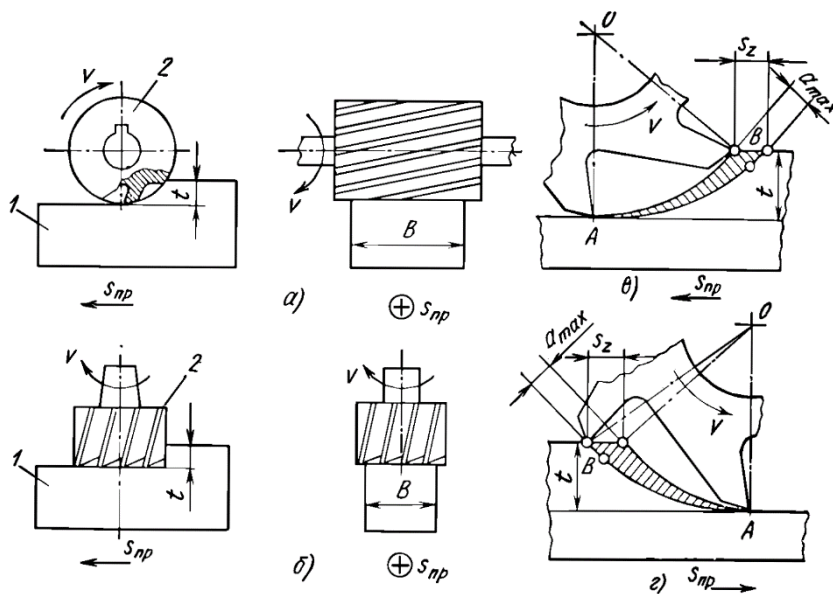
Схеми фрезерування циліндричною (а) і торцевою (б) фрезами, проти подачі (в) і по подачі (г): 1 – заготовка, 2 – фрези.
